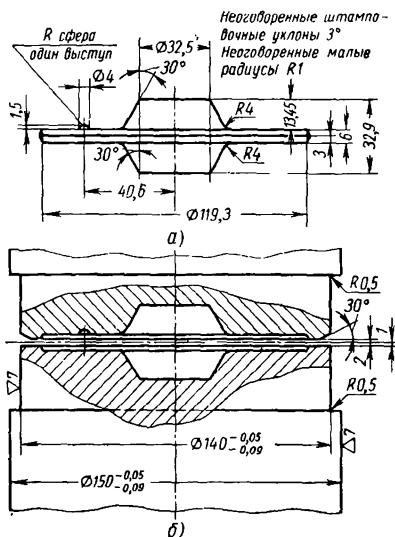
Поковка ступицы: а — чертеж поковки; б — вставка для штамповки
